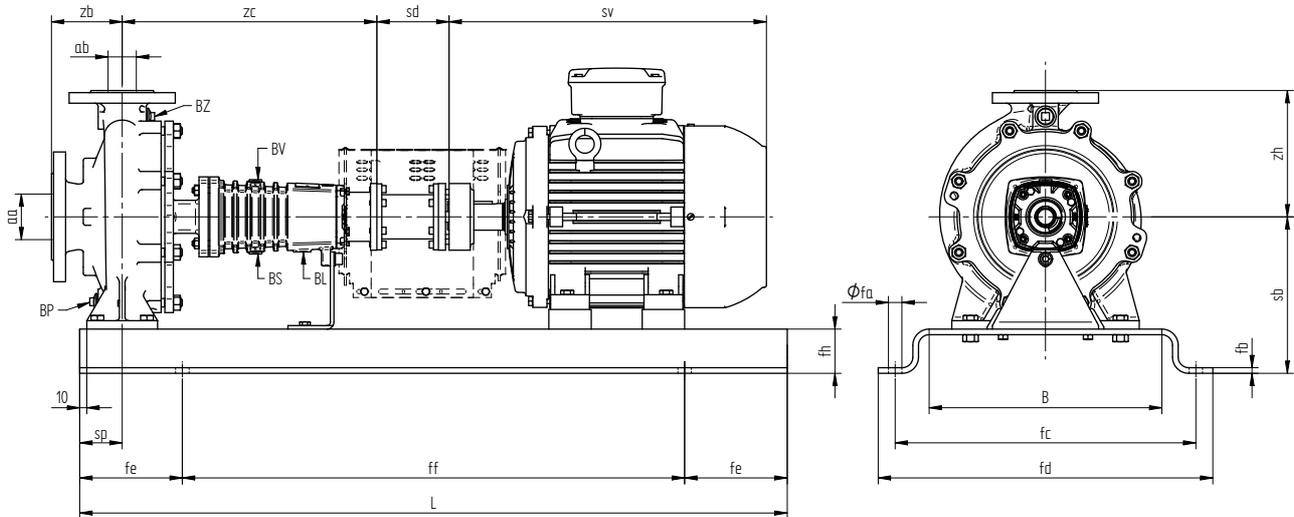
Unidad del motor de la bomba con acoplamiento con separador.
